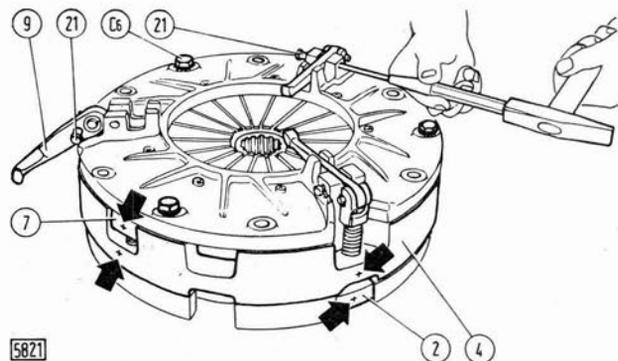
Démontage des axes (21) d'articulation des leviers de débrayage (9) du couvercle de l'ensemble.
